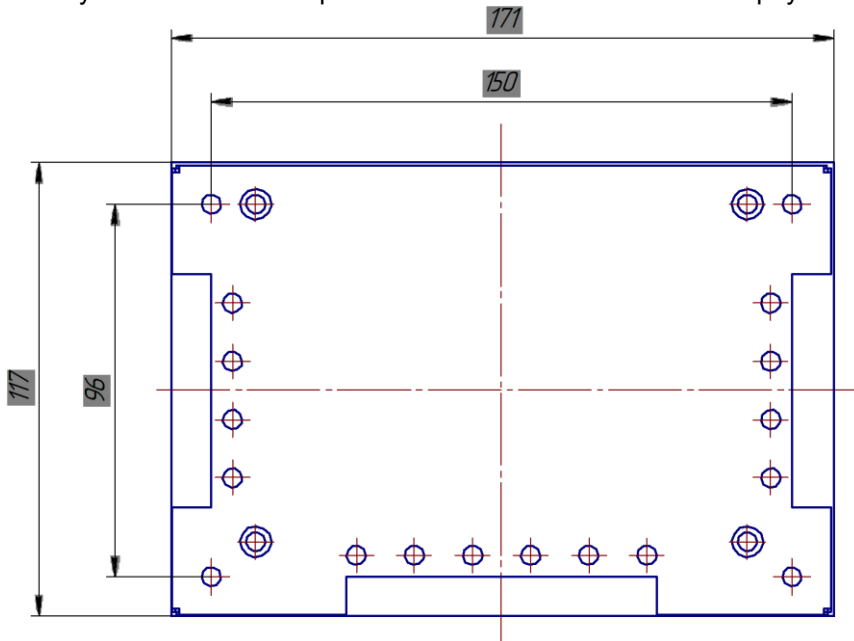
Разметка крепления АПИ в металлическом корпусе.
